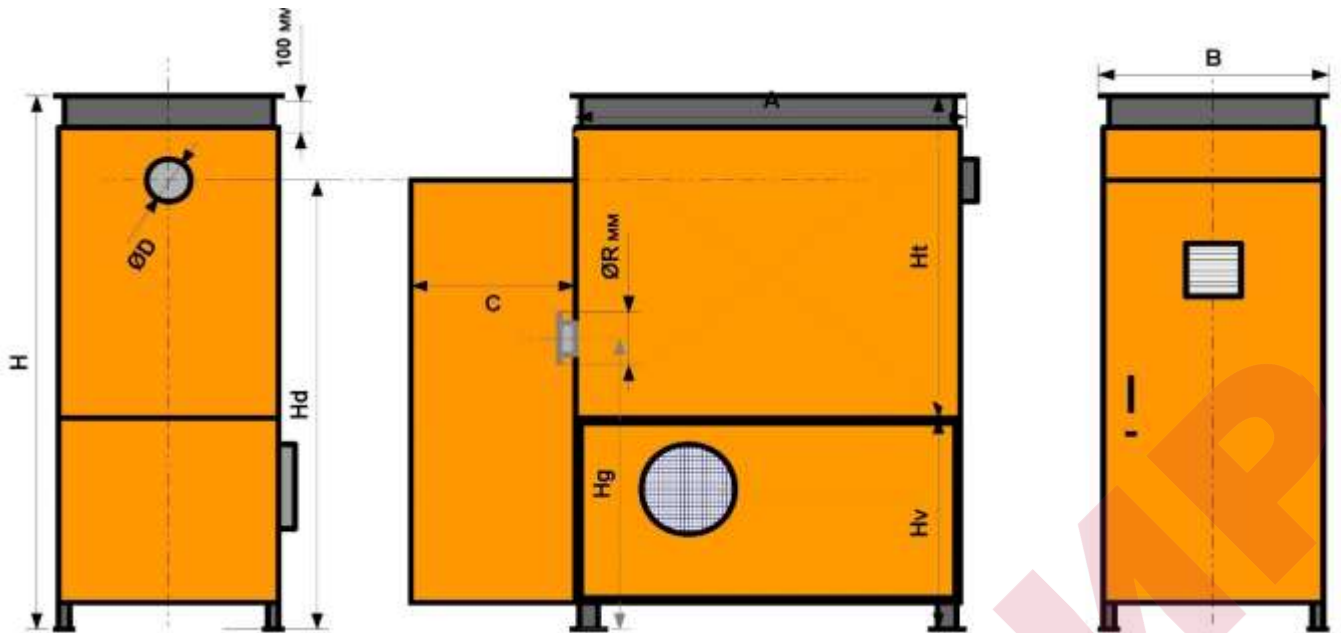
Габаритные размеры воздухонагревателей серии VT-PT
